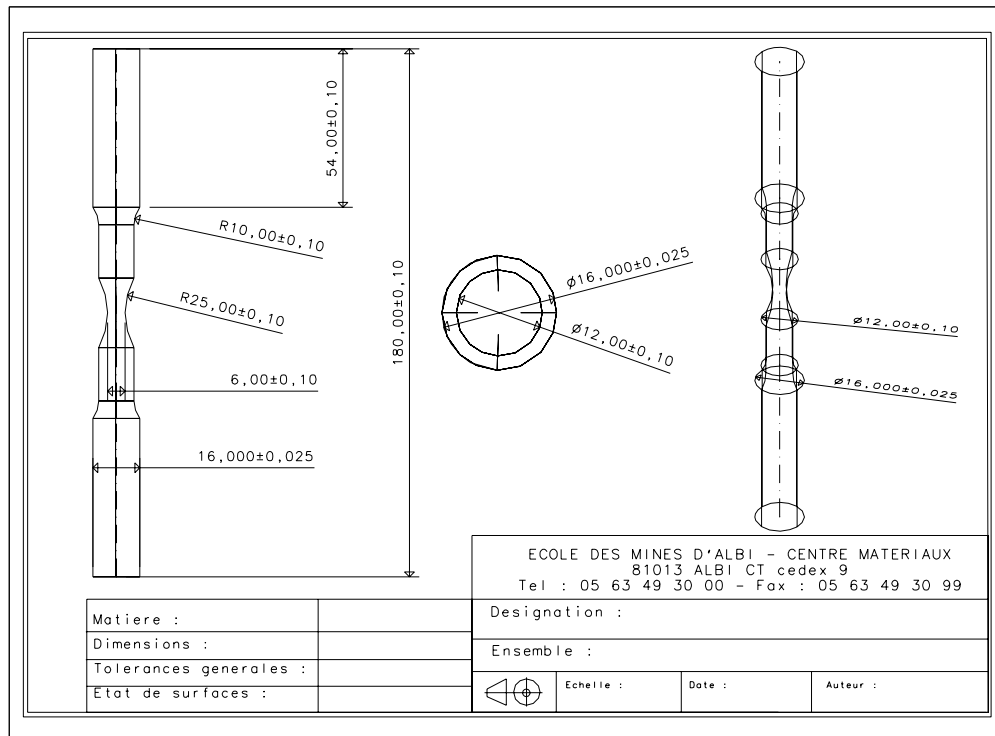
Géométrie d'éprouvette pour un rayon d'entaille de 25mm et un K_t de 1.05
